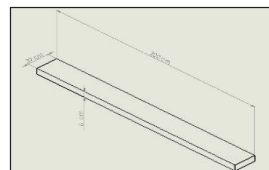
Plano Pieza 2: paleta Mecánica. Fuente: Elaboración propia
